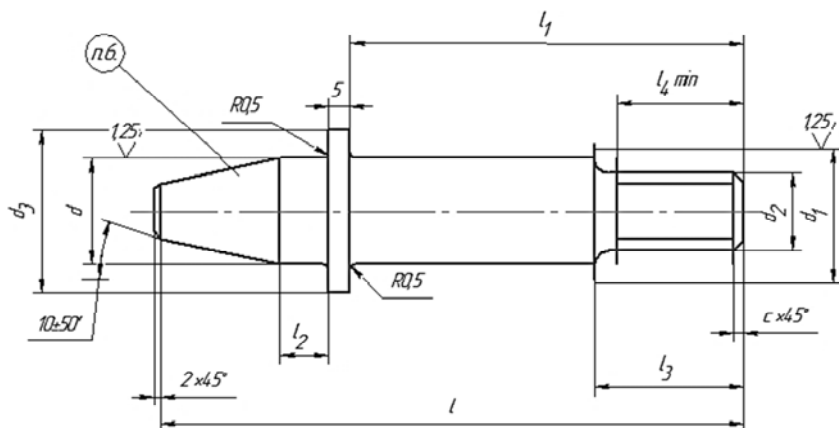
Направляющий штырь для металлических форм с параллельным разъемом
